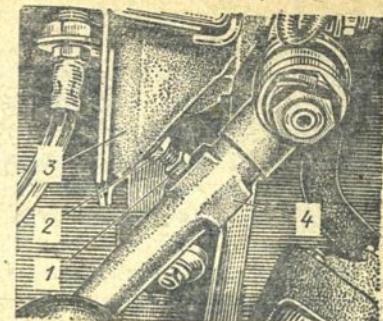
Узел регулировки максимального угла поворота переднего колеса:
